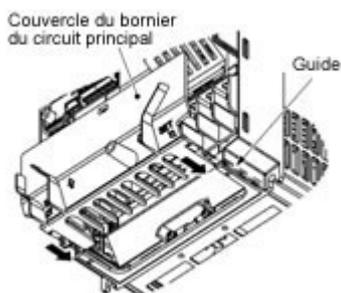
Montage du couvercle du bornier du circuit principal
